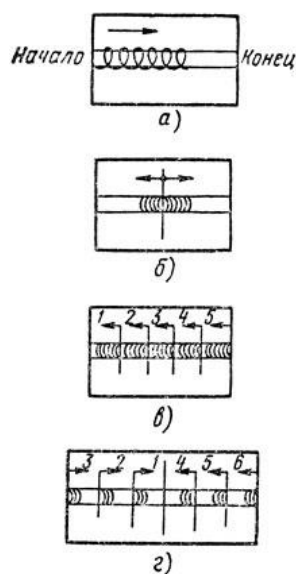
Схема сварки швов различной конец протяженности: а - сварка на проход для выполнения коротких соединений; б - сварка соединений средней длины от середины к концам шва; в - сварка обратноступенчатым способом для выполнения соединений средней длины (1 - 5 - последовательность наложения швов); г - сварка обратноступенчатым способом от середины к концам шва для выполнения длинных соединений
